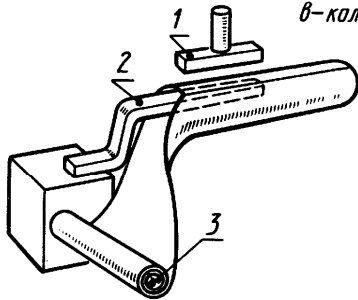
Схема сварки ПВХ рукавов и шлангов из пленки продольным швом
